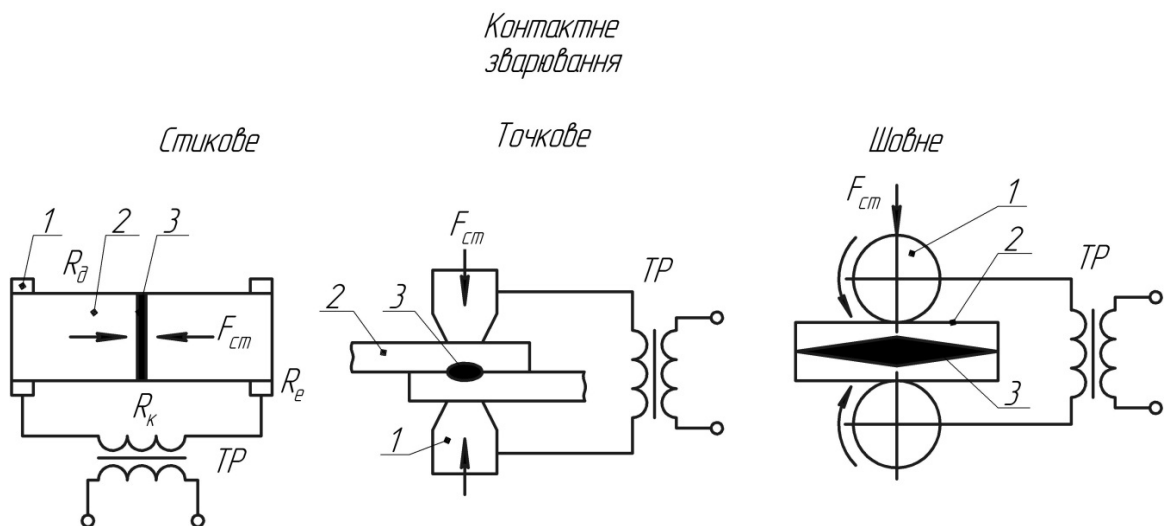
Види електроконтактного зварювання: 1 - охолоджувані водою електроди; 2 - деталі, що зварюються; 3 - місце зварювання
